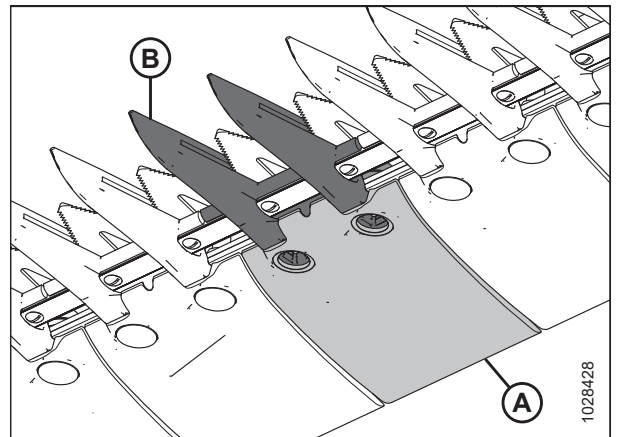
Загострений протиріжучий палець ножа й захисна пластина
